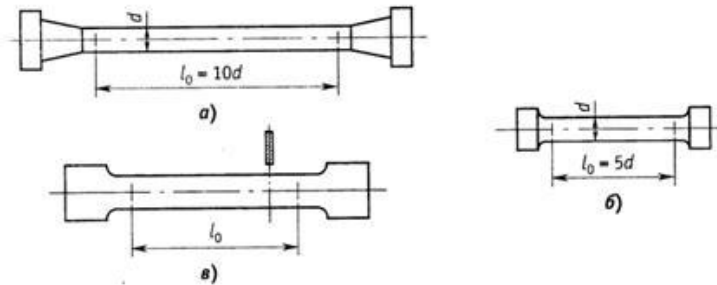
Цилиндрический образец для испытаний на растяжение
